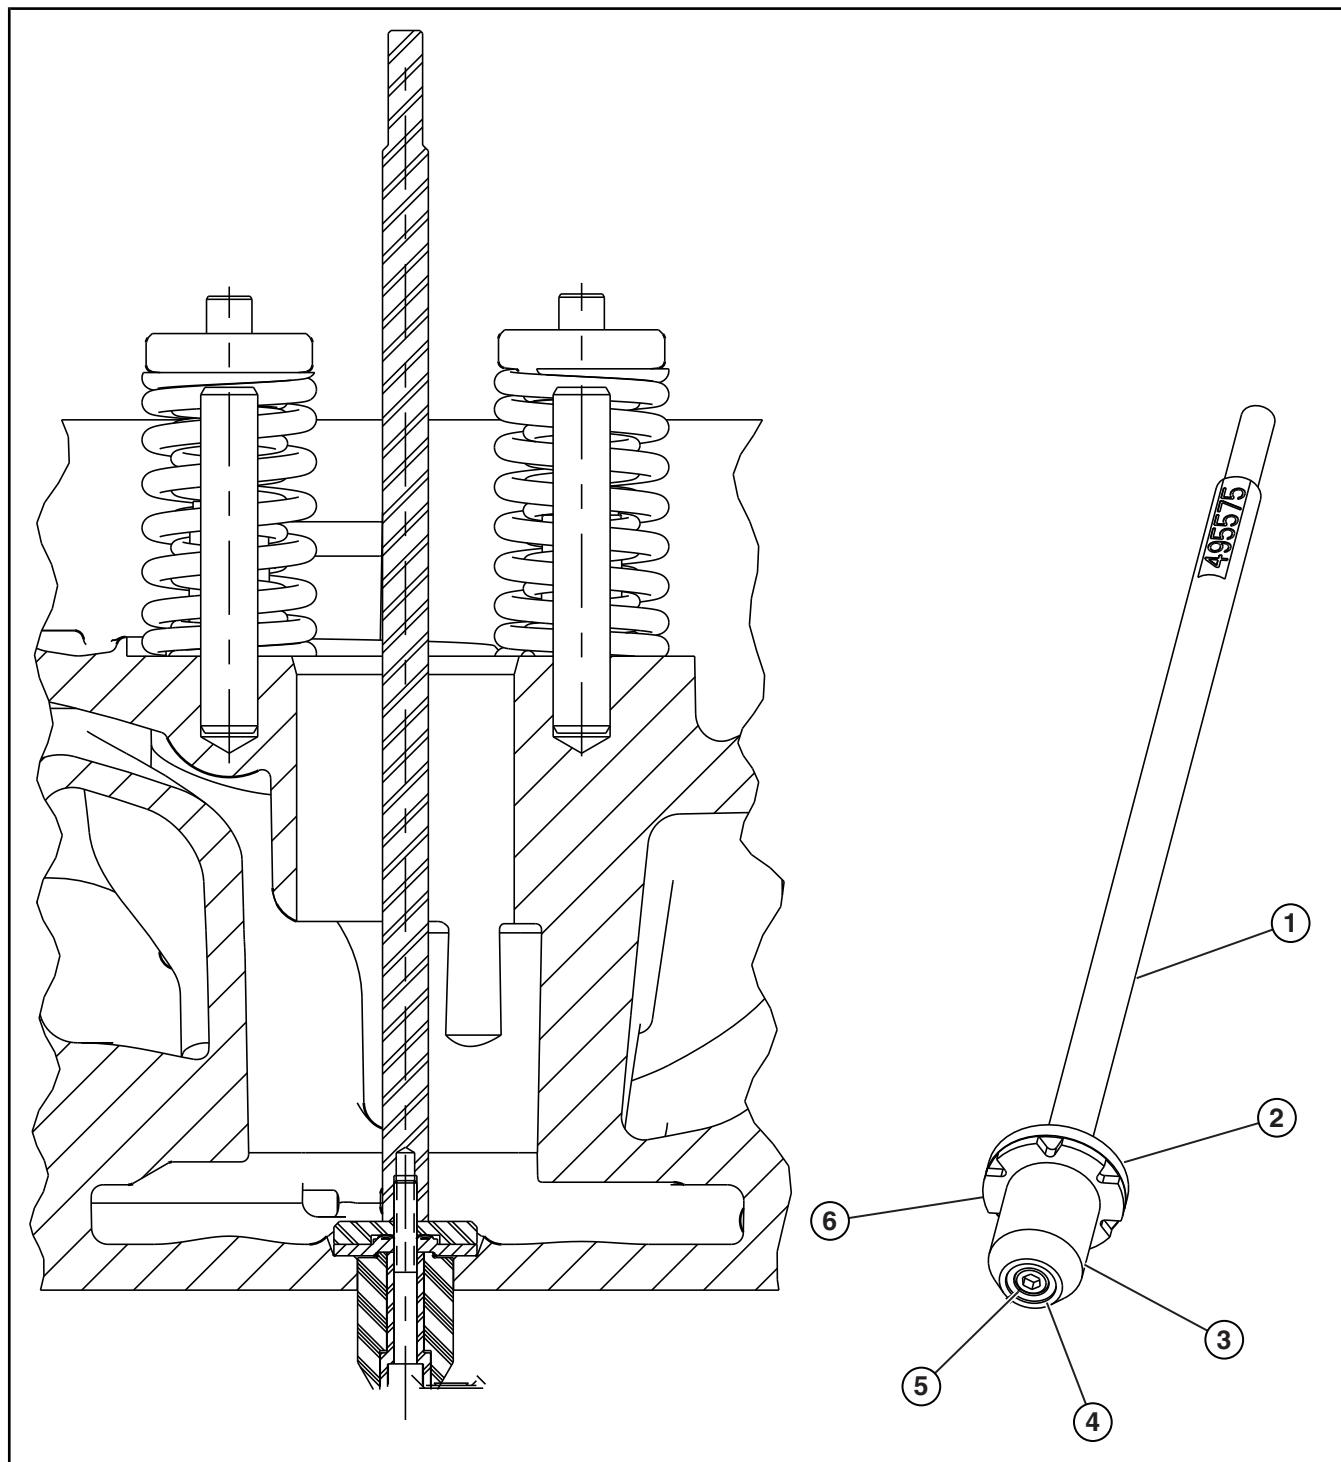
Инструмент для обработки поверхности посадочного места втулки свечи зажигания
